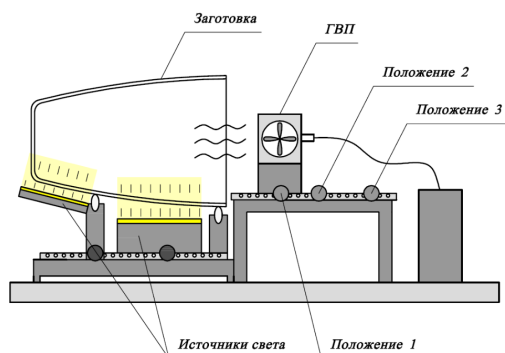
Схема способа подготовки поверхности изделия для ВОК (составлено авторами)
